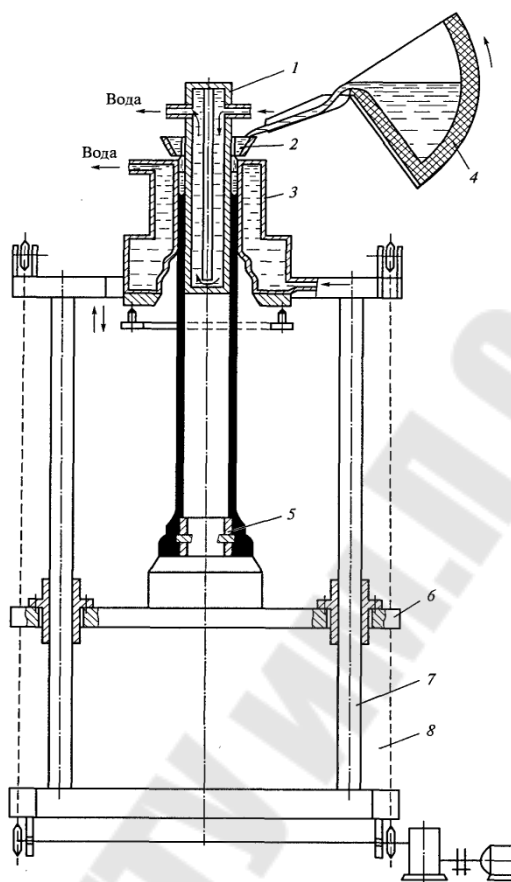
Установка полунепрерывного литья труб: 1- водоохлаждаемый стержень; 2- литниковая система; 3- кристаллизатор; 4- дозирующий ковш; 5- разборный стержень с кольцевым выступом; 6- стол; 7- колонны; 8- цепь привода стола
